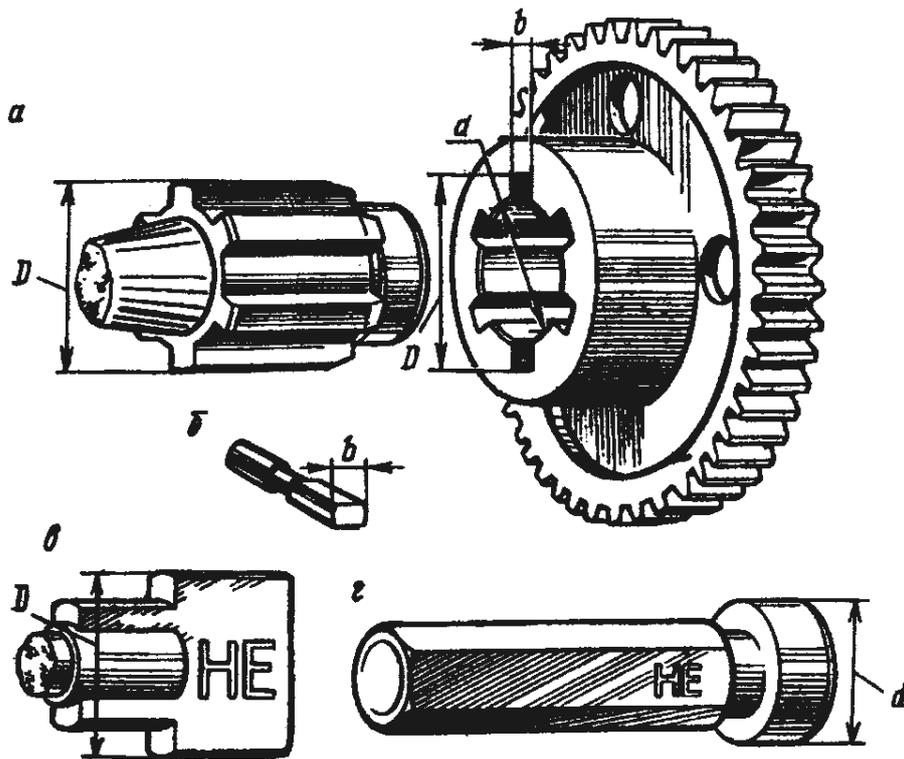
Калибры-пробки для контроля шлицевого прямобочного отверстия:
